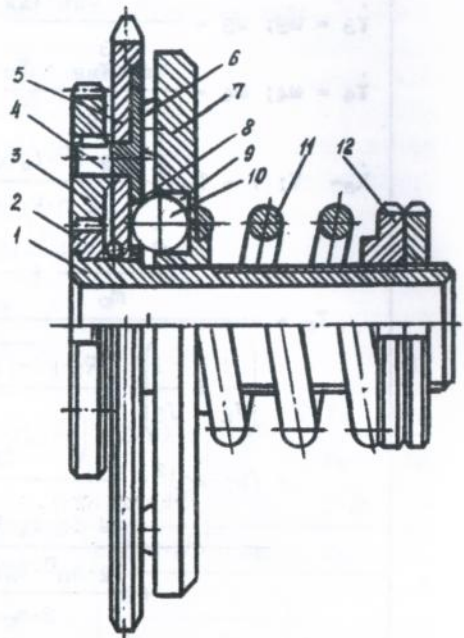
Однорядний планетарно-кульковий керуючий пристрій
